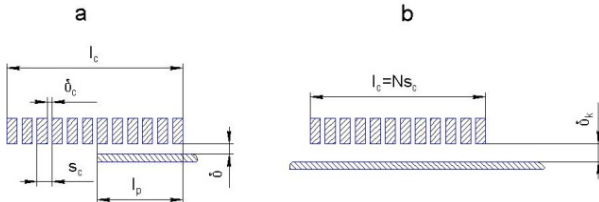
Схема для расчёта приведённой величины зазора между индуктором и заготовкой
